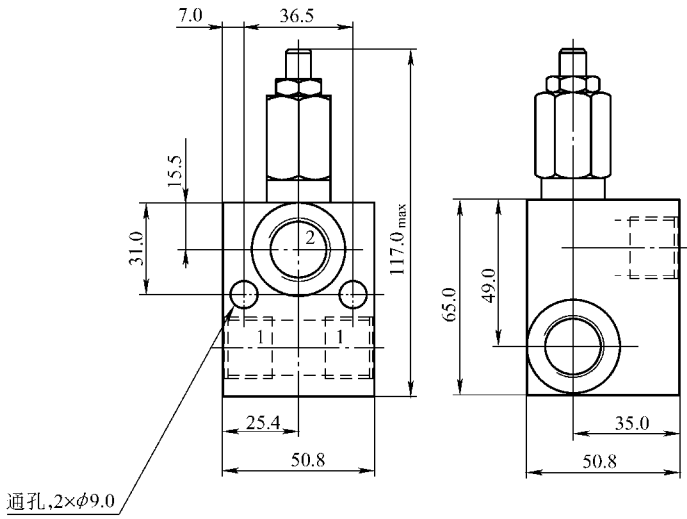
1AR60 型插芯及阀组外形尺寸
